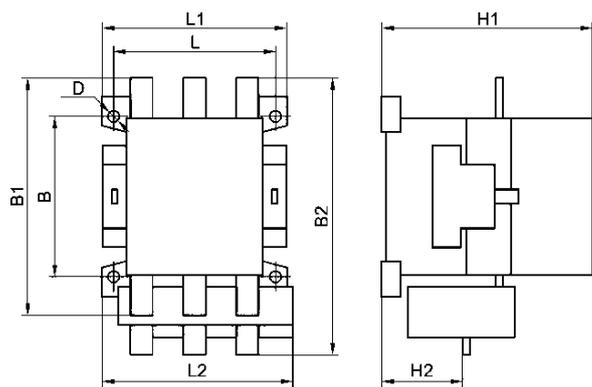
Пускатель нереверсивный ПМА-5000, ПМА-6000, IP00
